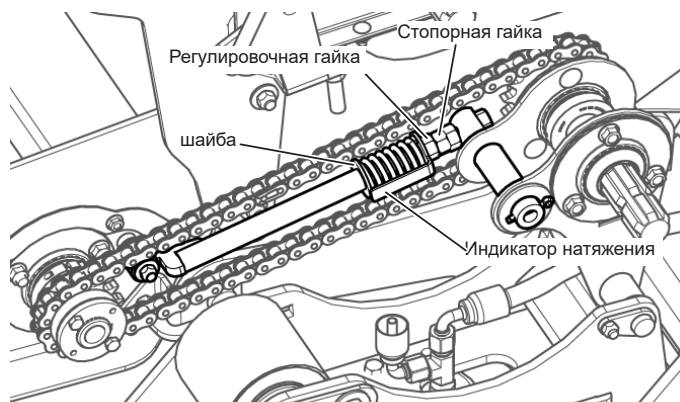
Регулировка натяжения приводной цепи центрального транспортера
